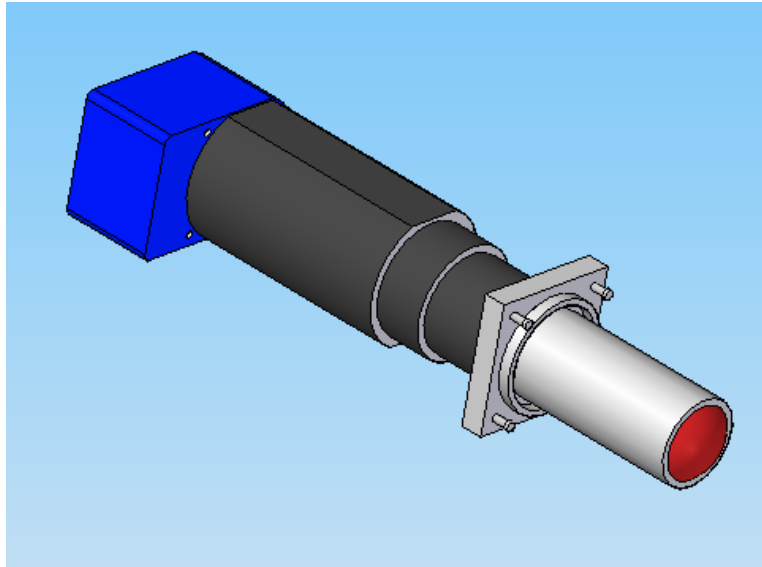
Motor MR615 30Q con reductora diseñado en Solid Edge.
